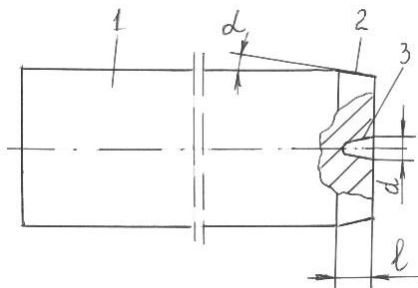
Заготовка з підготовленою конічною ділянкою на зовнішній поверхні переднього конуса і центрувальним отвором на передньому торці. Позначення у тексті.
